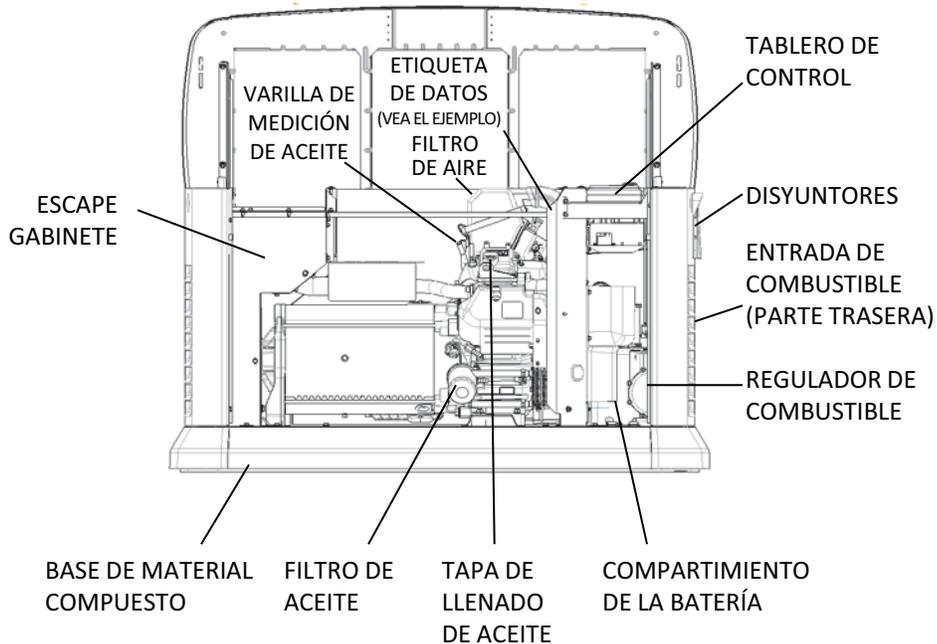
Unidad de 10 y 13 kVA, motor GT-990
